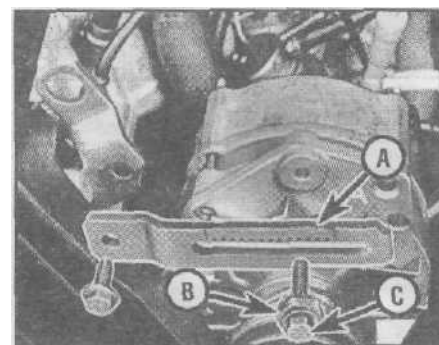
Проверка натяжения ремня привода генератора
